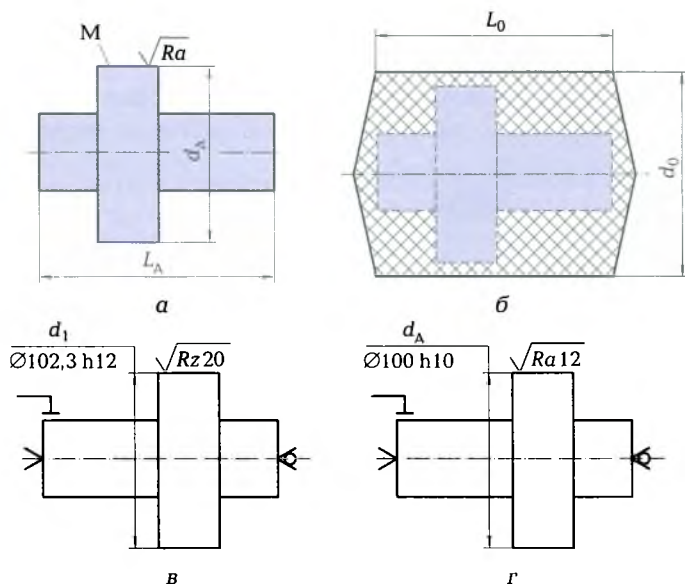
Схема расчета общего припуска на наружную цилиндрическую поверхность:
